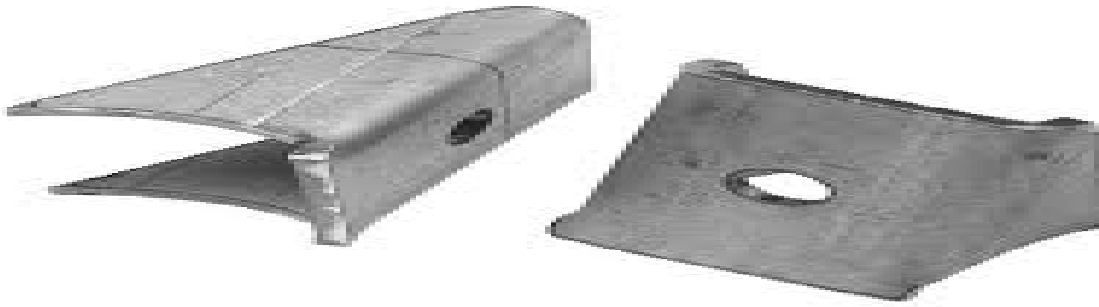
Tipo Weld Tabs a utilizar
